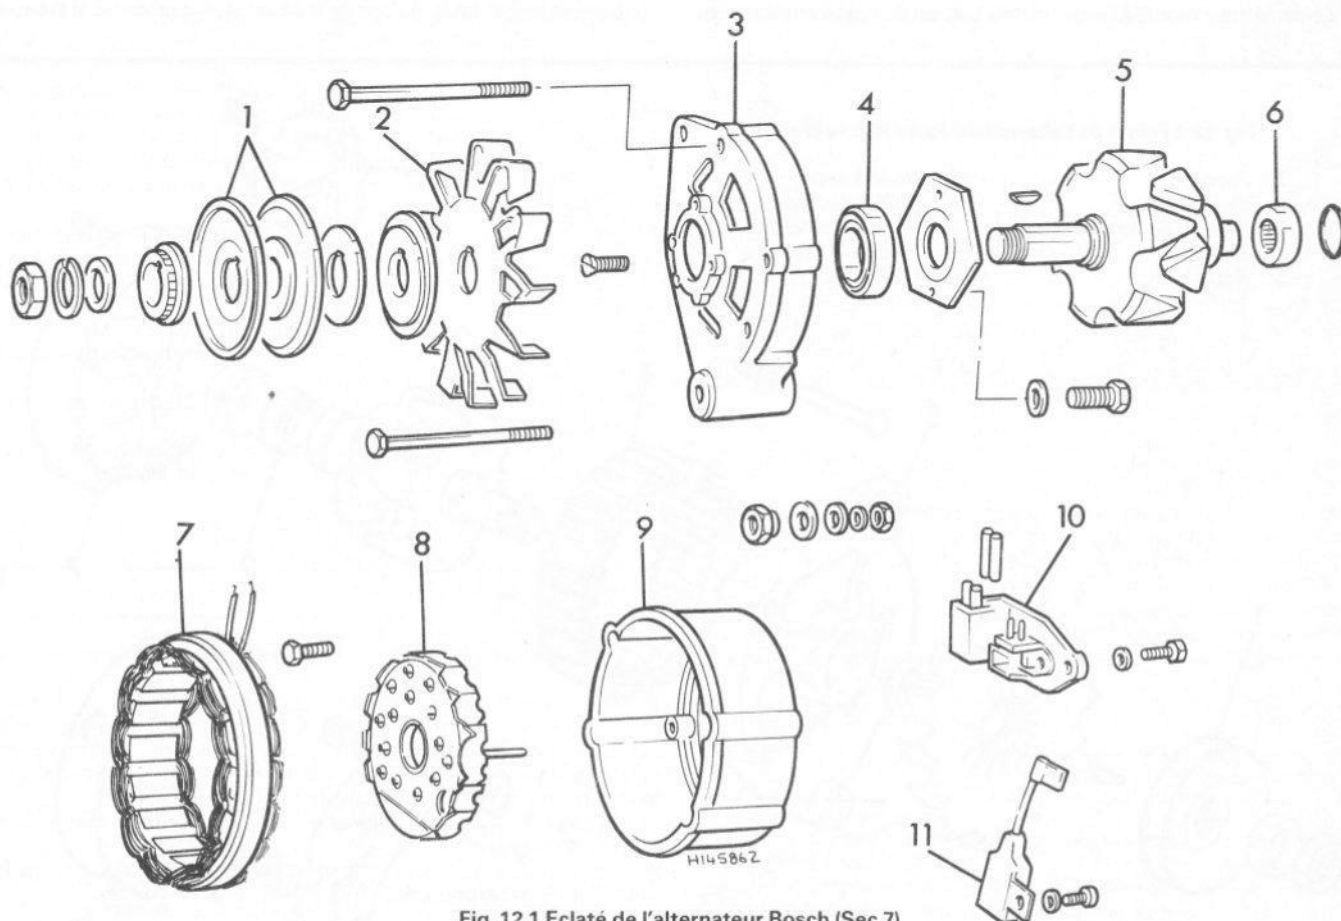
Eclaté de l'alternateur Bosch (Sec 7)
